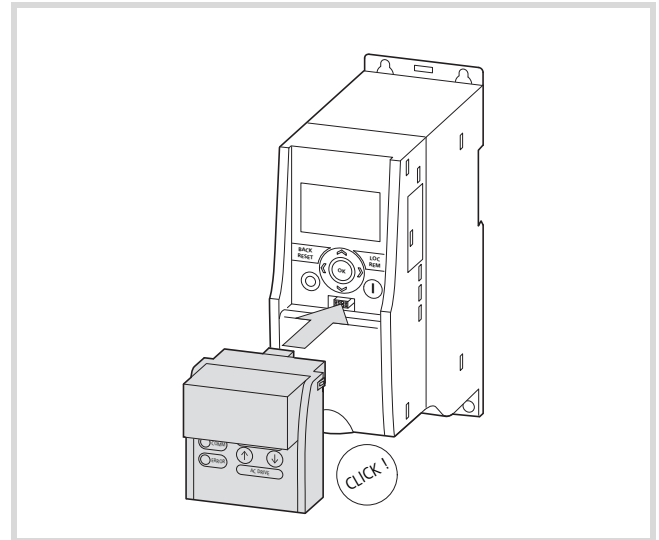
Ausschaltgruppe MMX-COM-PC aufstecken
